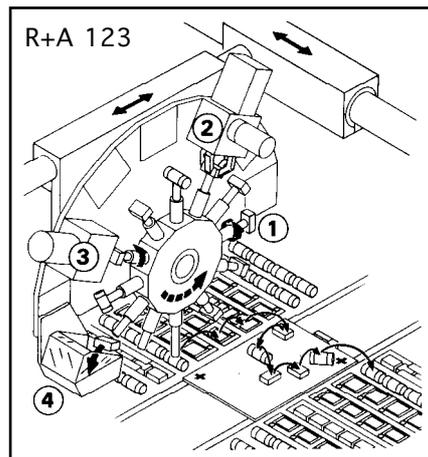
Machine rapide pour assemblage CMS (Siemens)
